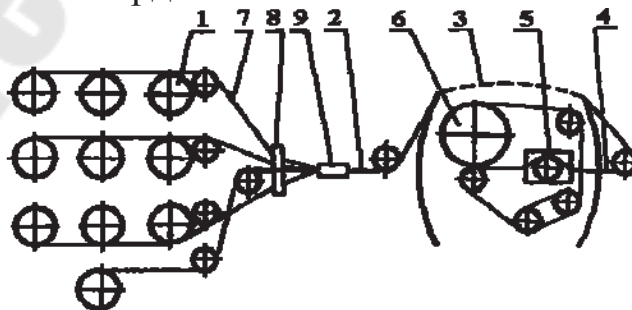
Кинематическая схема свивочной машины двойного кручения с внешним расположением питающих катушек («снаружи-вовнутрь»): 1 – питающая катушка; 2 – первичная свивка; 3 – «баллон»; 4 – вторичная свивка; 5 – торсионный узел; 6 – приемная катушка; 7 – проволока; 8 – распределительный шаблон; 9 – плашки
